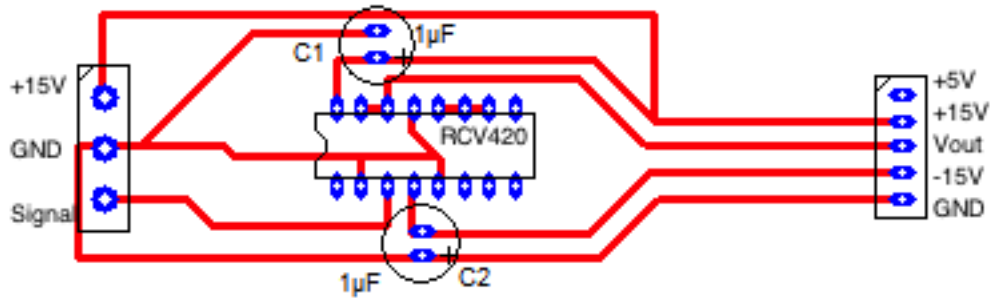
PCB de la tarjeta CAS sensor de ph.
